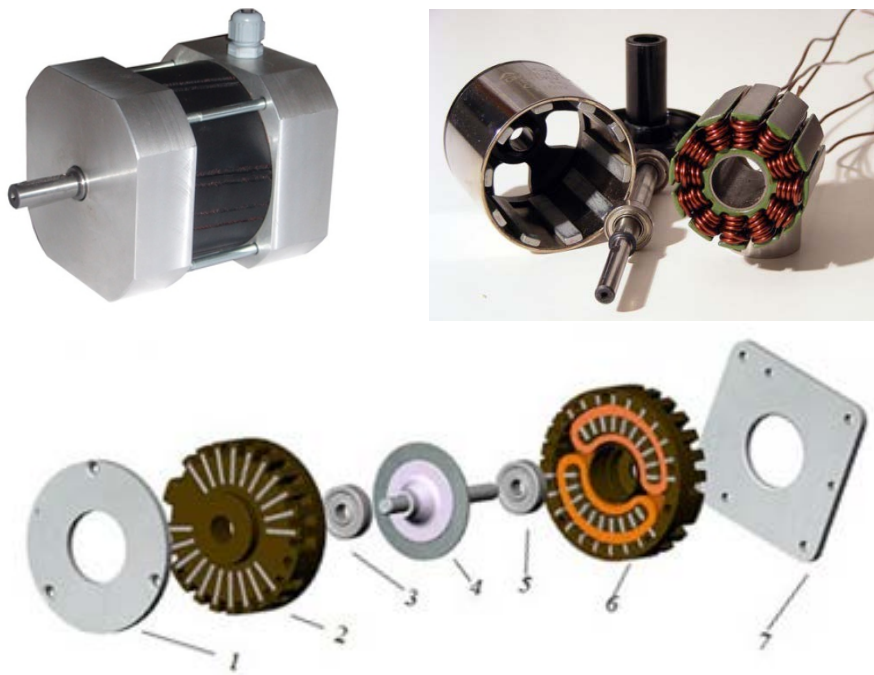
Вентильний двигун: а – зовнішній вигляд; б – елементи двигуна у розібраному вигляді; в – схема. 1 – задня частина корпусу; 2 – статор; 3, 5 – підшипники; 4 – магнітний диск (ротор); 6 – статор з обмоткою; 7 – передня частина корпусу
